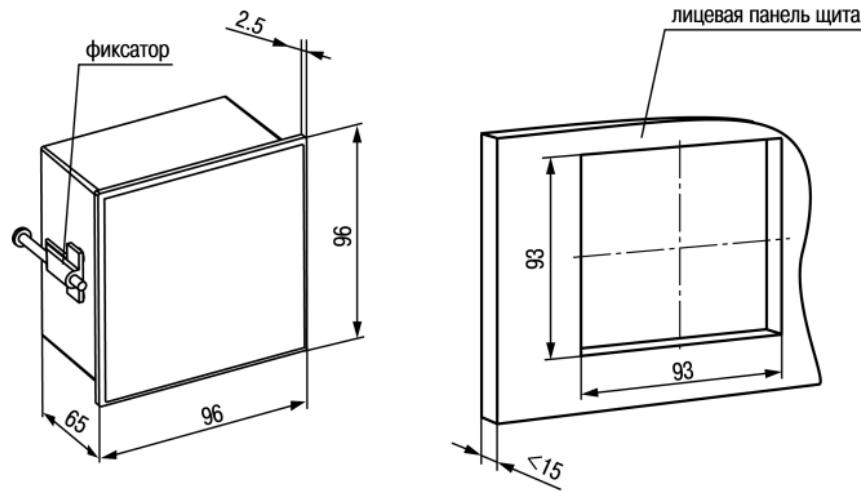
Габаритные размеры корпуса Щ1
